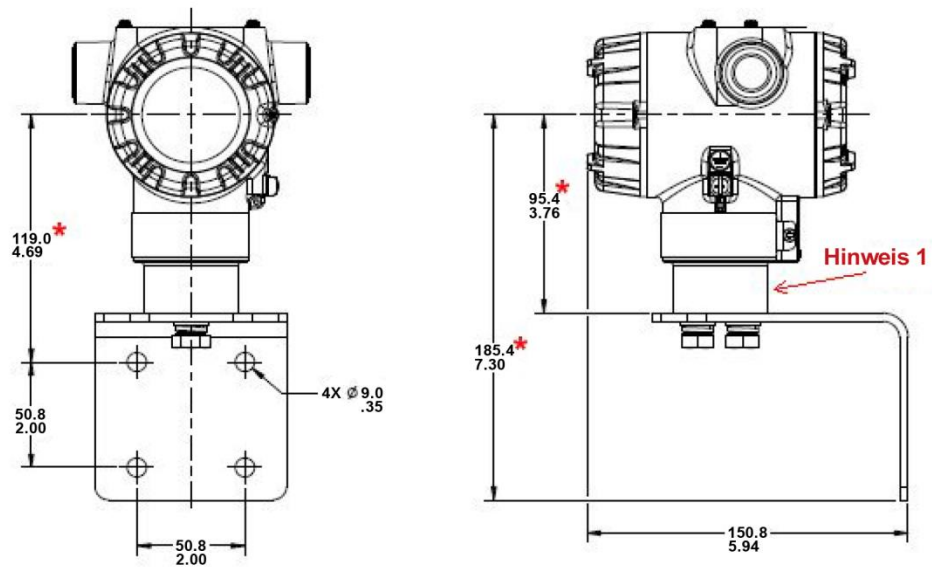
STT750 mit Adaptergehäuse - Horizontale Wandmontage
